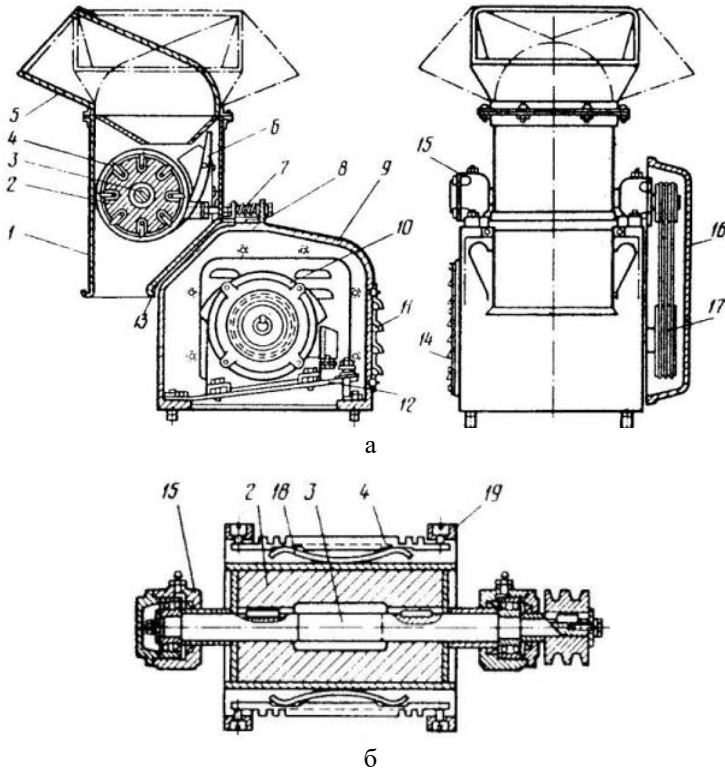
Схема ножової дробарки КДП – 4М: а – загальний вид; б – осьовий розріз барабана; 1 – корпус; 2 – ножовий барабан; 3 – вал; 4 – ножі; 5 – бункер; 6 – колодки; 7 – пружинні амортизатори; 8 – гайки; 9 – корпус; 10 – електродвигун; 11, 14 – щитки; 12 – похила плита; 13 – лоток; 15 – підшипникові вузли; 16 – щиток; 17 – клинопасава передача; 18 – плоскі пружини; 19 – кільця з регульовальними гвинтами
